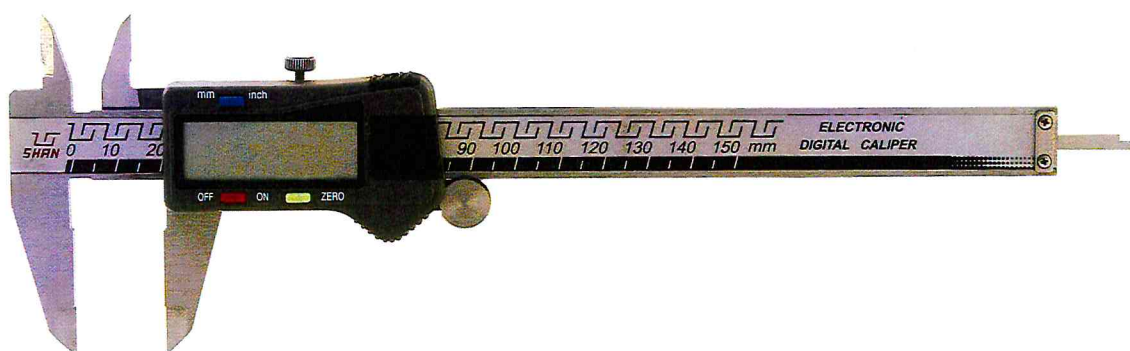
Общий вид штангенциркулей двусторонних с глубиномером с цифровым отсчетным устройством
